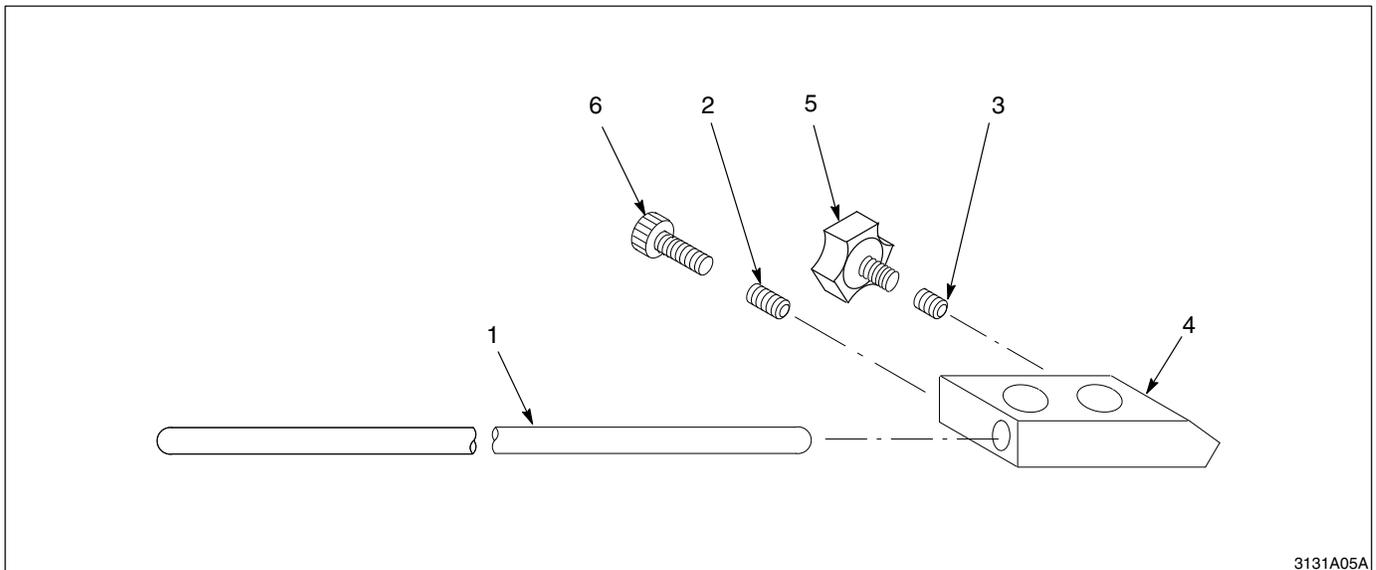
Kit collecteur d'ions, montage sur rotule en ligne
